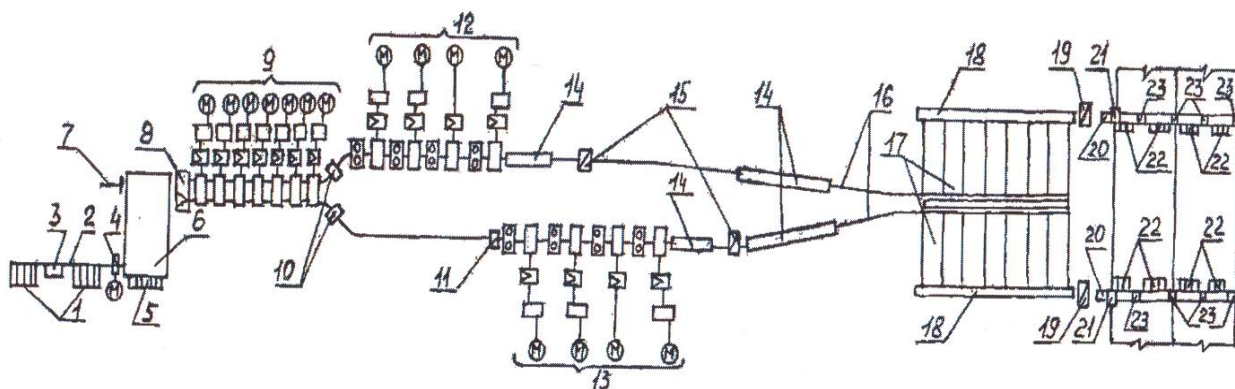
Схема розташування устаткування безперервного дрібносортового стану 250-2: 1 – завантажувальні ґрати; 2 – підвідний рольганг; 3 – кишень для забракованих заготовок; 4 – втаскувач; 5 – штовхач; 6 – нагрівальна піч; 7 – виштовхувач; 8 – розподільник заготовок; 9 – чорнова група клітей; 10 – аварійні ножиці; 11 – обривний ніж; 12, 13 – ліва та права чистові групи клітей; 14 – лінія прискореного охолодження; 15 – двохбарабанні ножиці; 16 – рольганг; 17 – холодильник; 18 – відвідний рольганг; 19 – ножиці; 20 – прибиральний рольганг; 21 – пересувний упор; 22 – ваги з кишнями; 23 – упори
